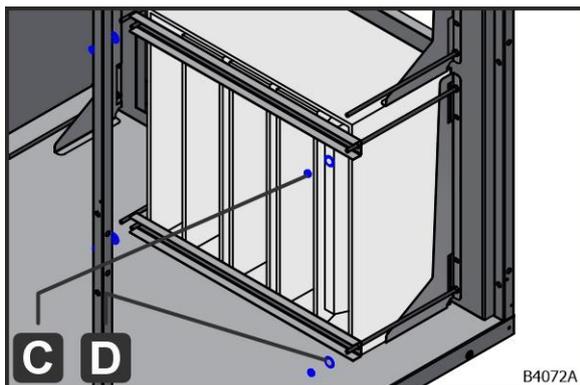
Scheibe (Q) und Sechskantmutter (C) aufschrauben
